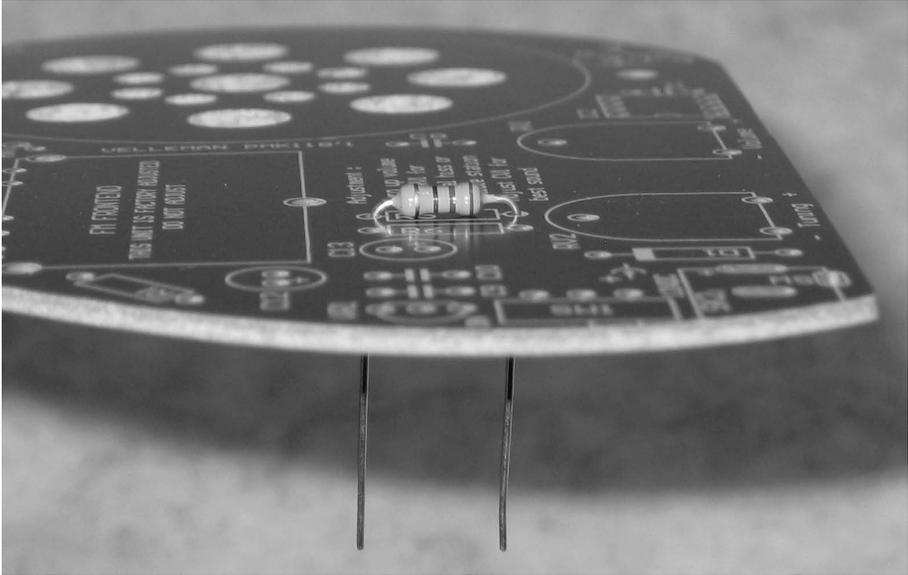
Ein fachgerecht eingebauter Widerstand.
